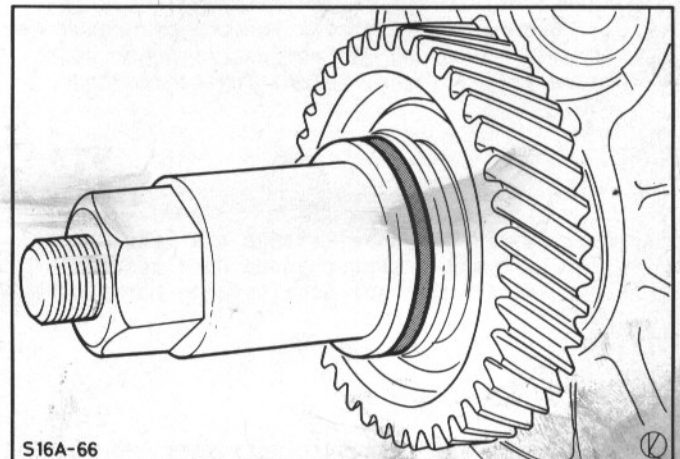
5. Gang-Zahnrad mit Spezialwerkzeug auf Vorgelegezahnradblock bringen
